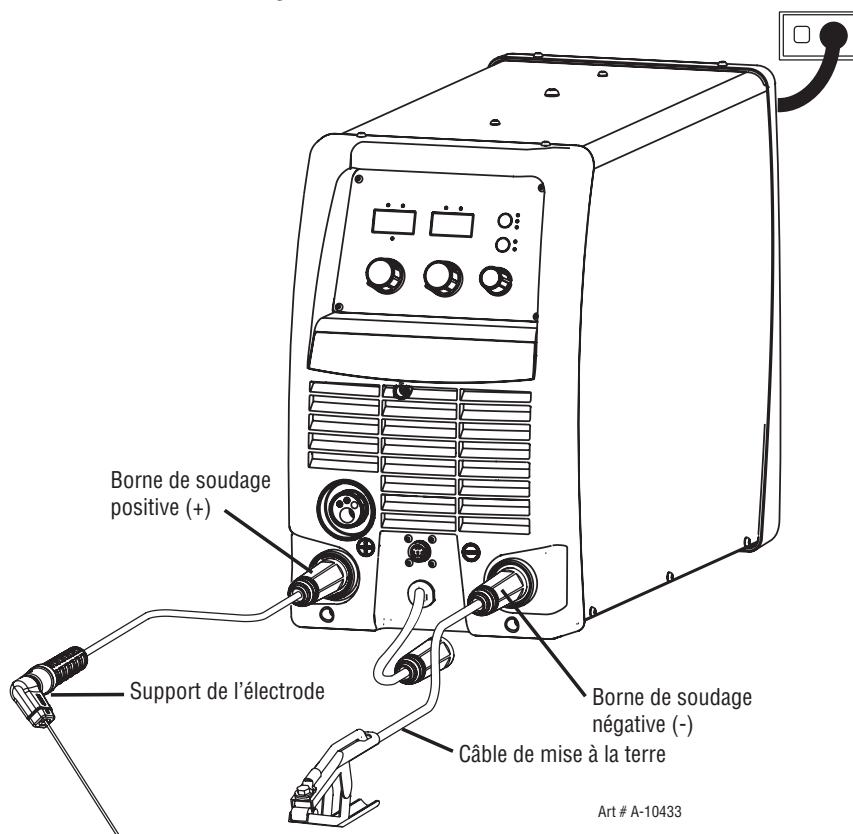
Configuration pour le soudage à l'arc manuel.
